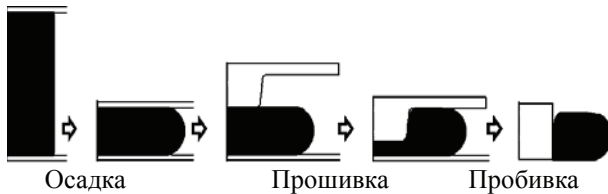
Последовательностьковки кольцевой заготовки из сплава ВТ6
